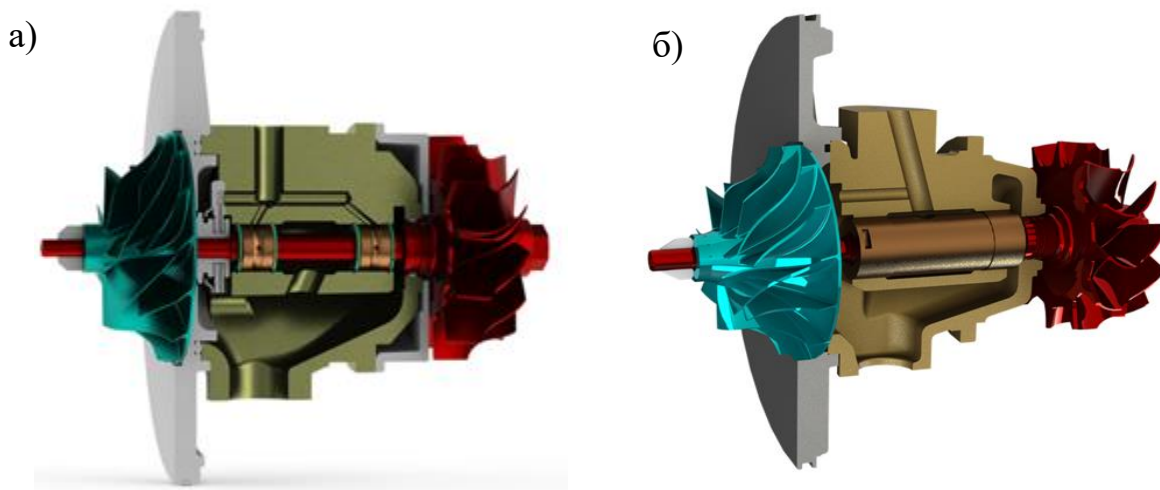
Конструктивные схемы подшипников ТКР:
